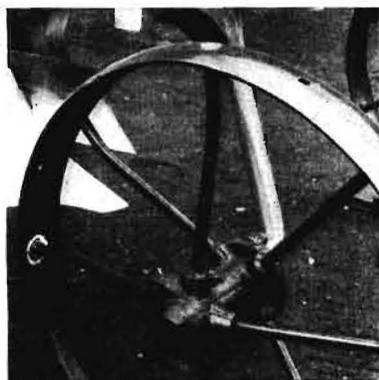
Auf der Felgeninnenseite verschweißte Speiche
